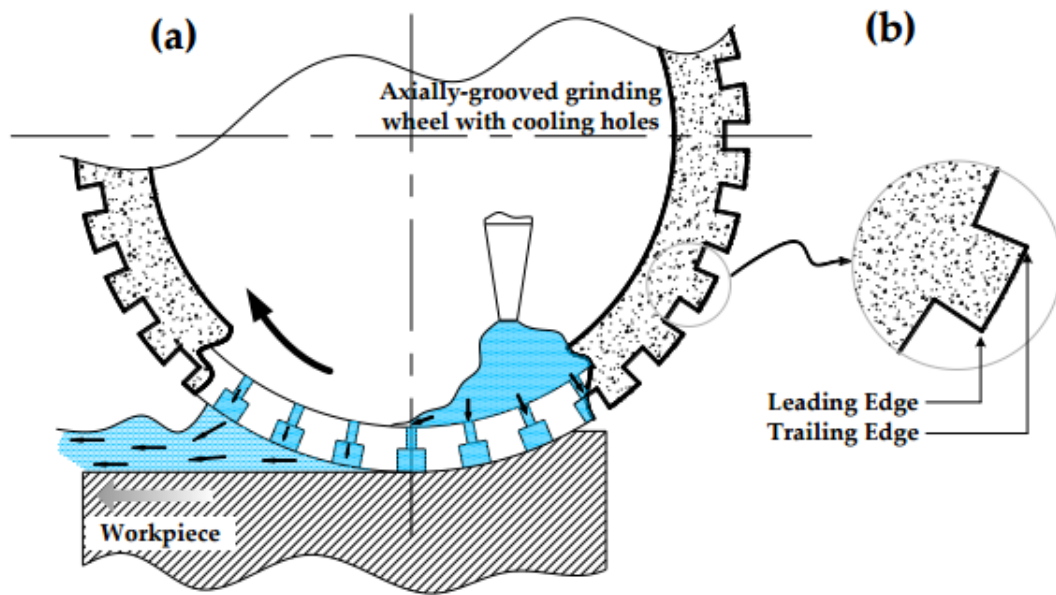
Конструкція шліфувального круга із канавками та отворами для охолодження на робочій поверхні круга [33]
